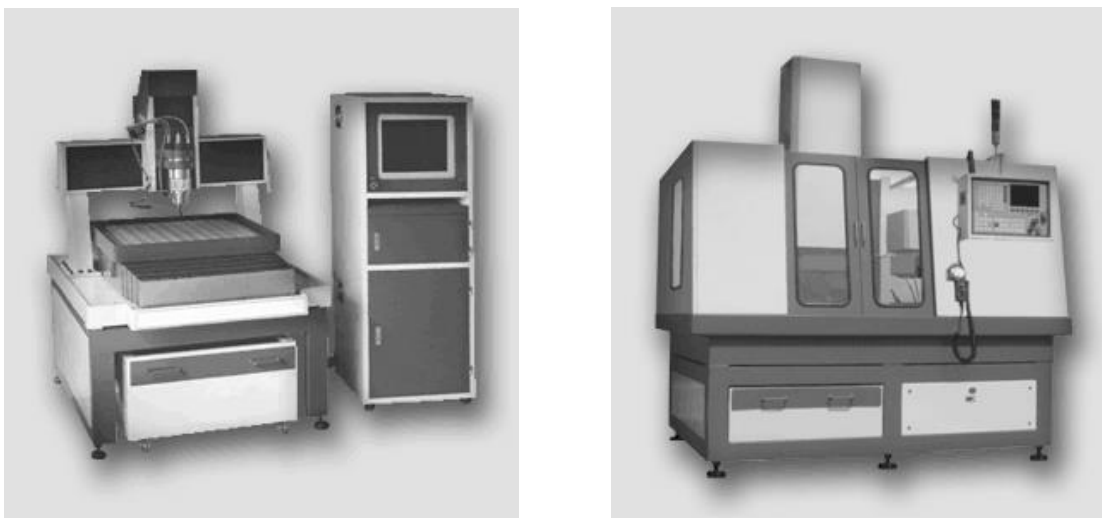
Гравірувально-фрезерні станки ROXA для 2D і 3D обробки
